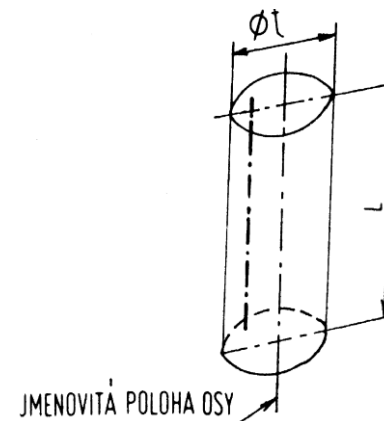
Vyobrazení tolerančního pole sklonu se značkou průměru [3]
